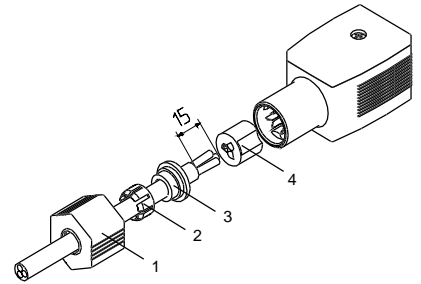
Gerätesteckdose Typ 2510/2511 INTERBUS Installationsbus, Draufsicht
